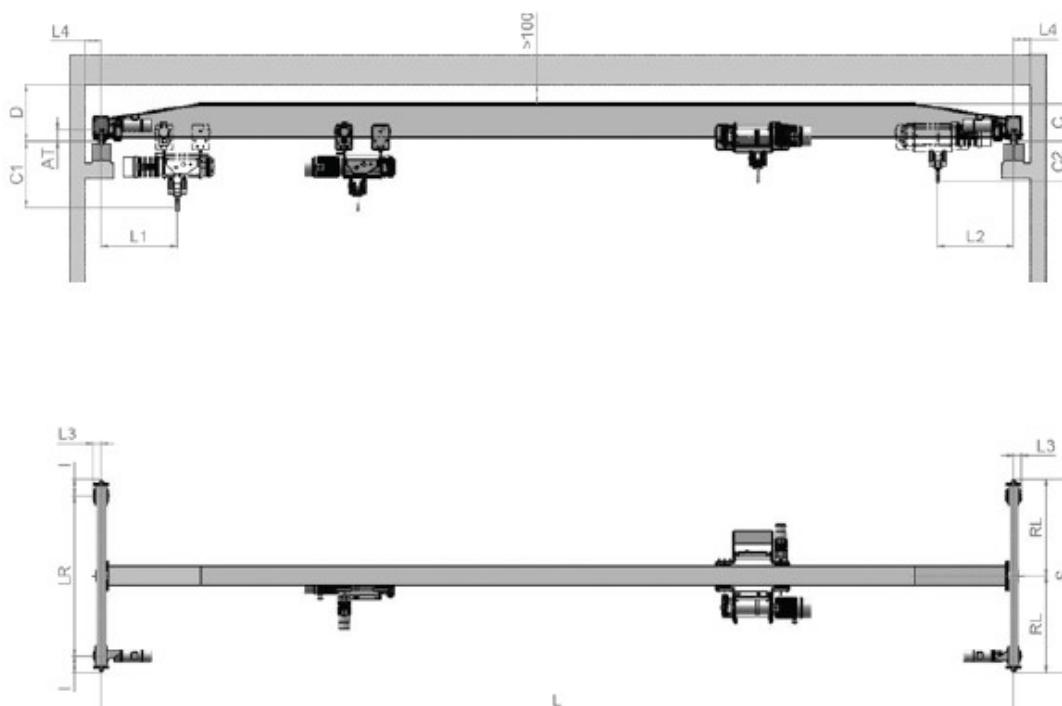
Alzado y planta de un puente grúa monorraíl
